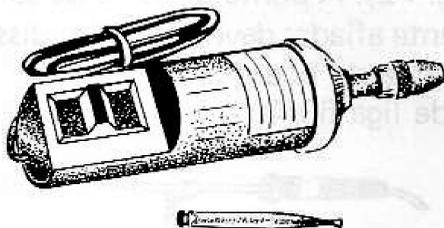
Mini furadeira elétrica para a furação de plaquetas de fenolite ou fibra de vidro.
